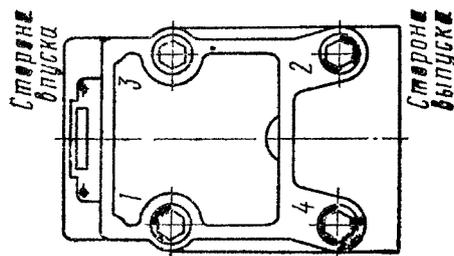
Порядок затяжки болтов крепления головок блока цилиндров
